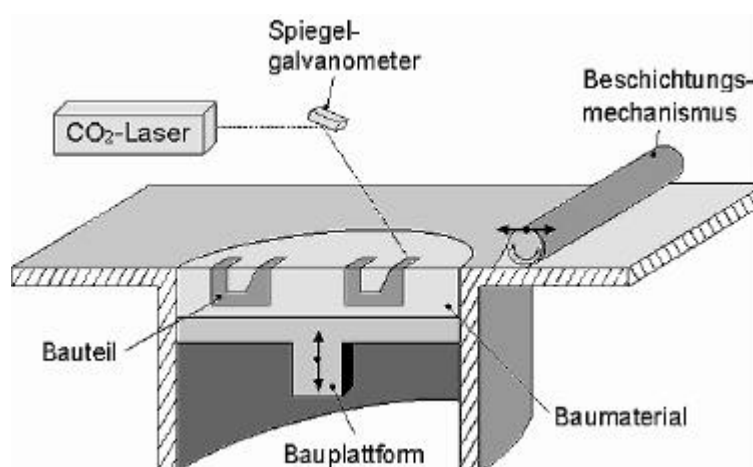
Prinzipieller Aufbau SLS-Maschine [RP-NET 2002]
